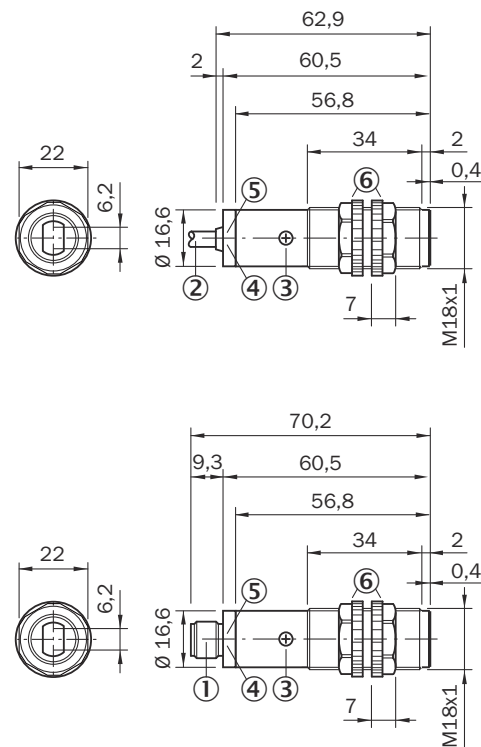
Maßzeichnung, Kunststoffgehäuse
